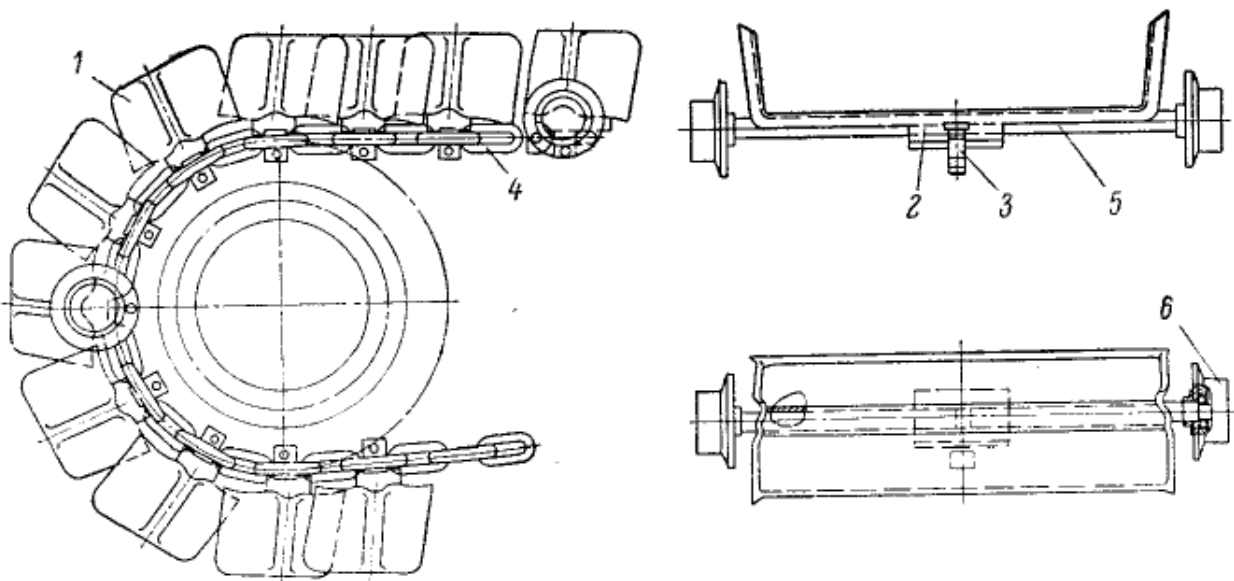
Пластинчасте полотно з короткими пластинами:
